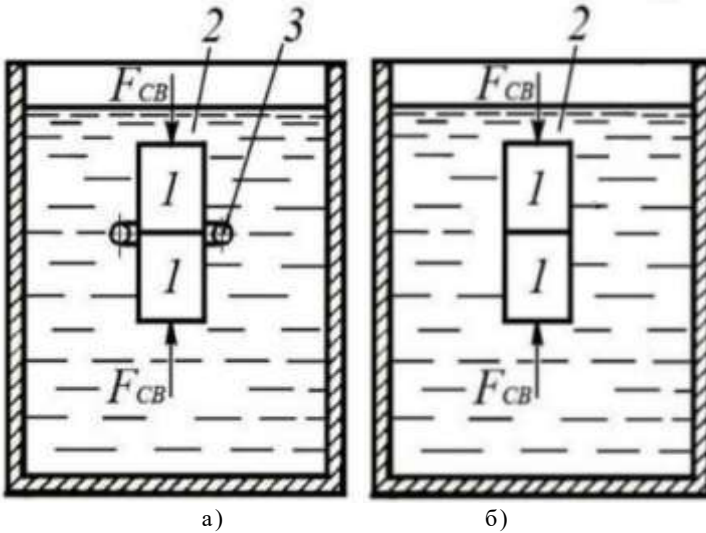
Схема дифузійного зварювання в рідкому середовищі: 1 – деталі, що зварюються; 2 – рідке середовище; 3 – індуктор
